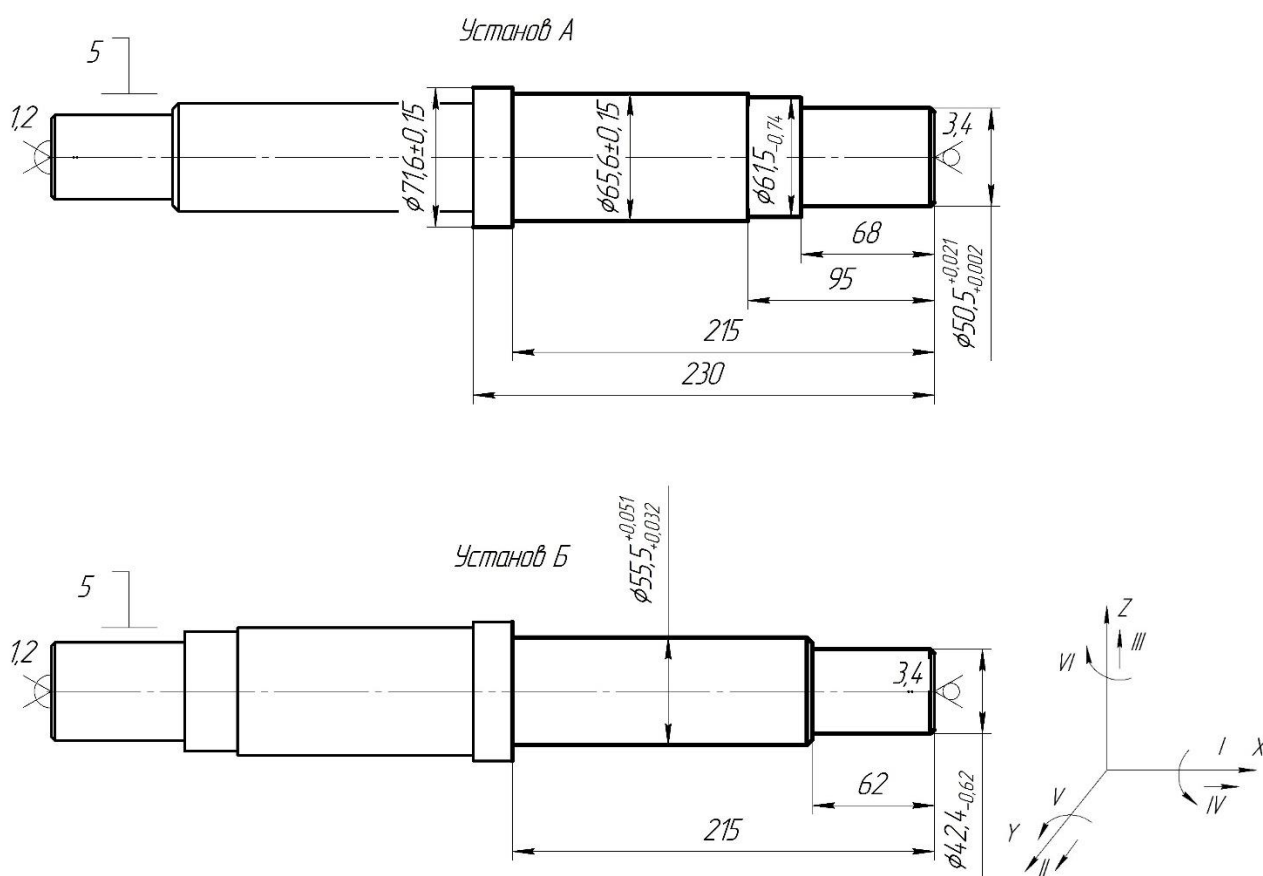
Схема базування заготовки в повідковому патроні
